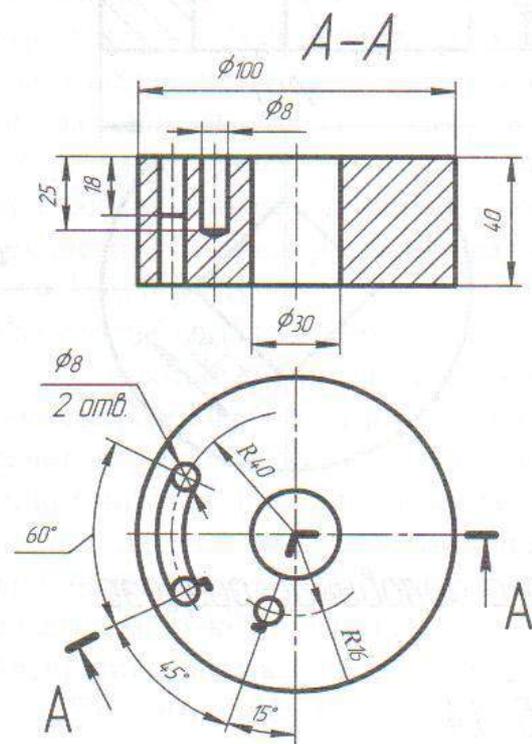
Ломанный разрез, переход по цилиндрической поверхности.
